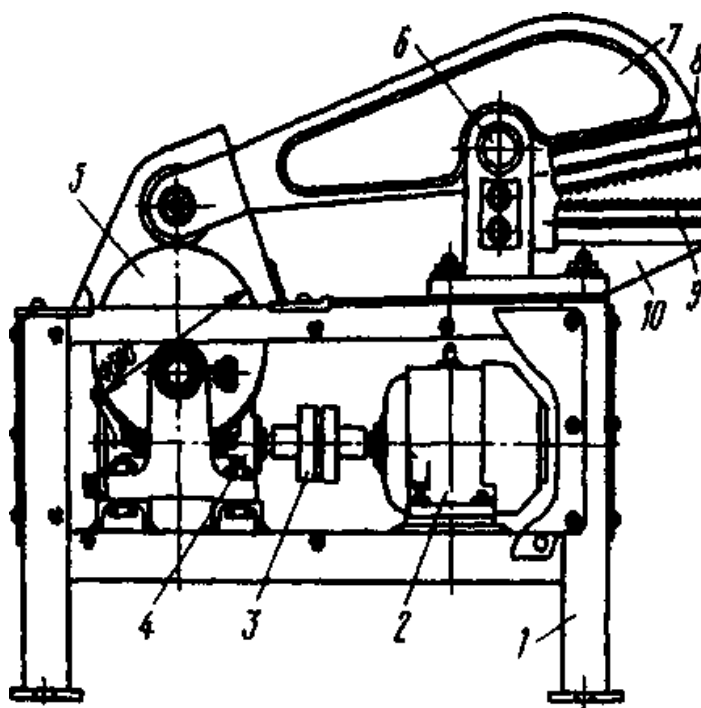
Машина для зняття копит МСК-1: 1 – станина; 2 – електродвигун; 3 – сполучна муфта; 4 – черв'ячний редуктор; 5 – ексцентрик; 6 – вісь балансира; 7 – балансир, 8 і 9 – рифлені плити; 10 – опора нижньої рифленої плити
